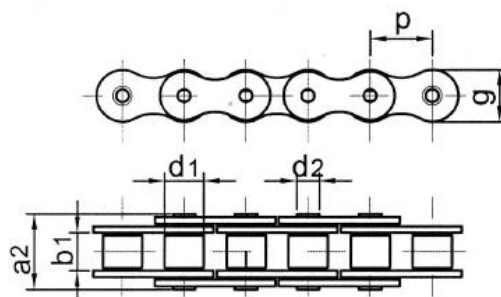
Cadena simple de rodillos ISO 606 04-1 fabricante Causer [10]
